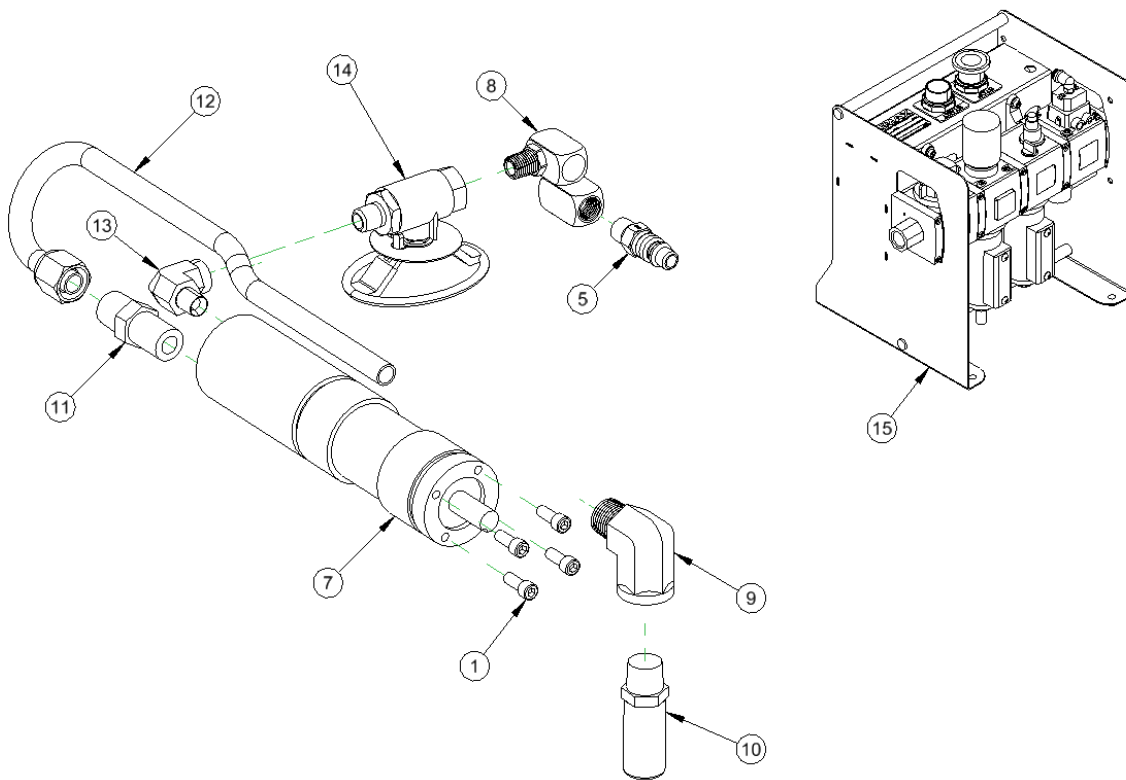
FF3000 Hauptgehäuse Baugruppe 2 (P/N 35686)
